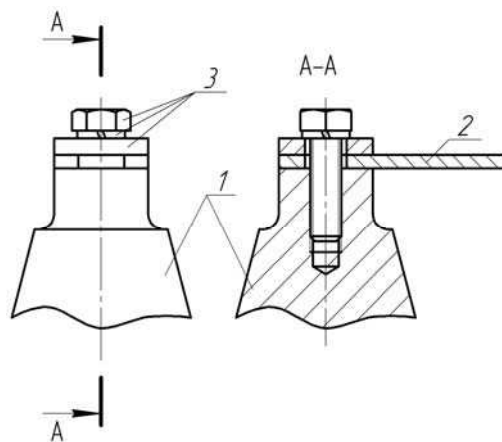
Устройство крепления образца винтом с прижимной планкой:
